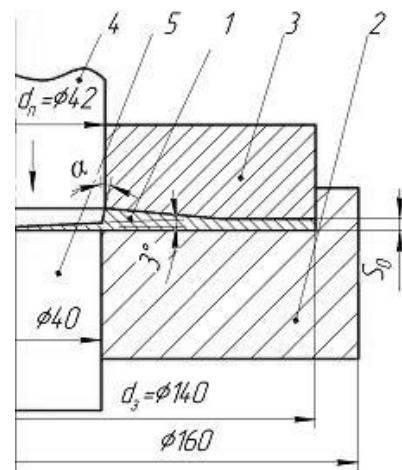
Схема формоутворення отвору і профілювання заготовки видавлюванням
